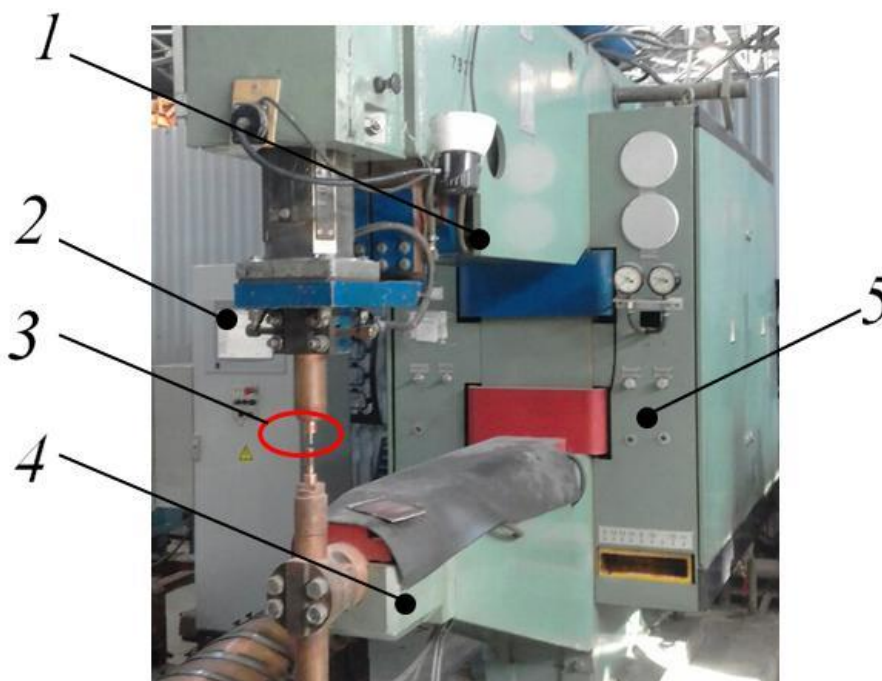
Машина контактной сварки МТВ-80.02-1:
